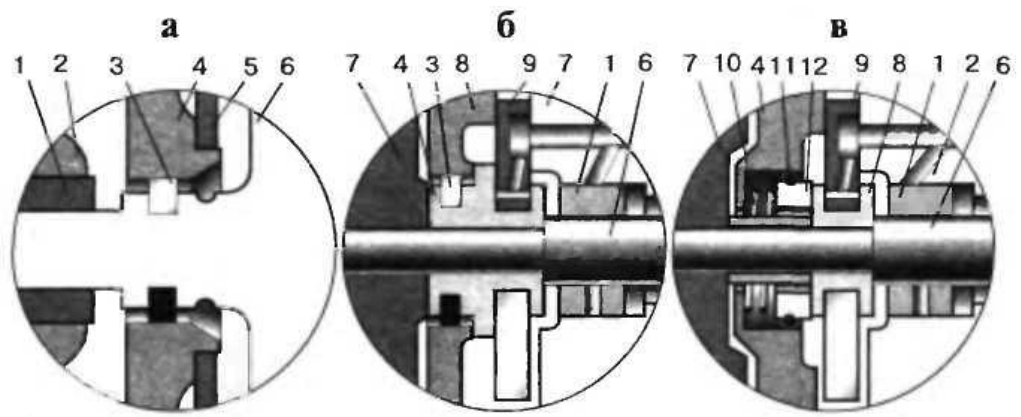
Візуалізація технічних рішень щодо конструкцій ущільнень ротора турбокомпресора: а - ущільнення з боку турбіни; б - ущільнення розрізним кільцем з боку компресора; в - торцеве ущільнення з боку компресора; 1 - втулка підшипника; 2 - корпус підшипників; 3 - ущільнювальне розрізне кільце; 4 - корпус ущільнення; 5 - кожух; 6 - ротор; 7 - колесо компресора; 8 - втулка під'ятника; 9 - під'ятник; 10 - пружина; 11 - гумове ущільнювальне кільце; 12 - графітове кільце
